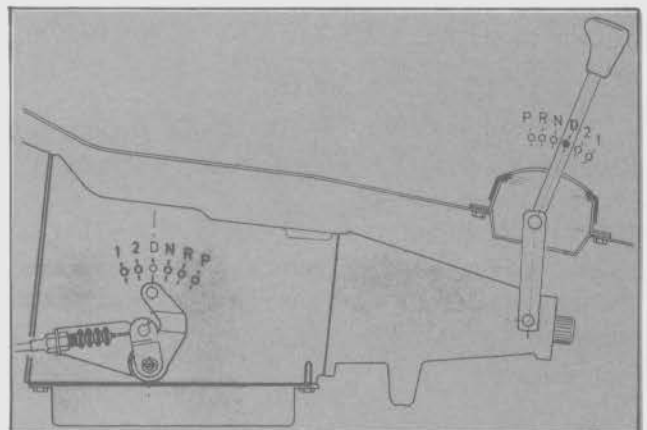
Posiciones de la palanca (D) durante el ajuste
